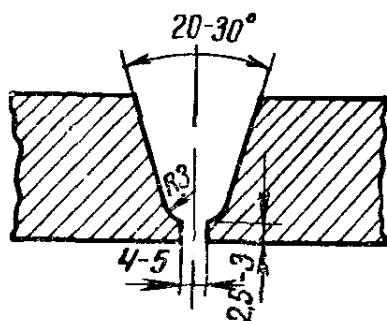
Подготовка кромок и сварка под флюсом нержавеющей хромоникелевой стали
